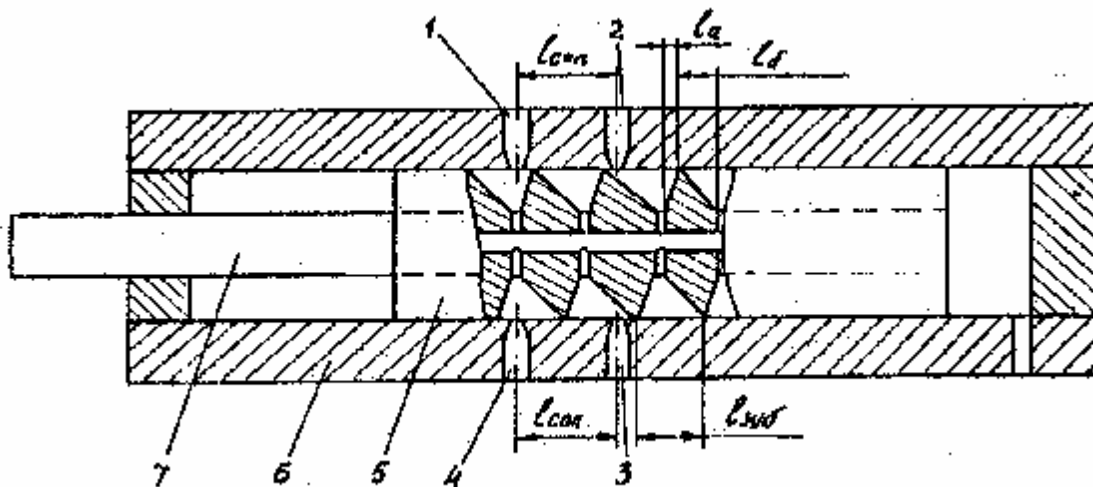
Двухтактный струйный шаговый гидроцилиндр с коническими впадинами
